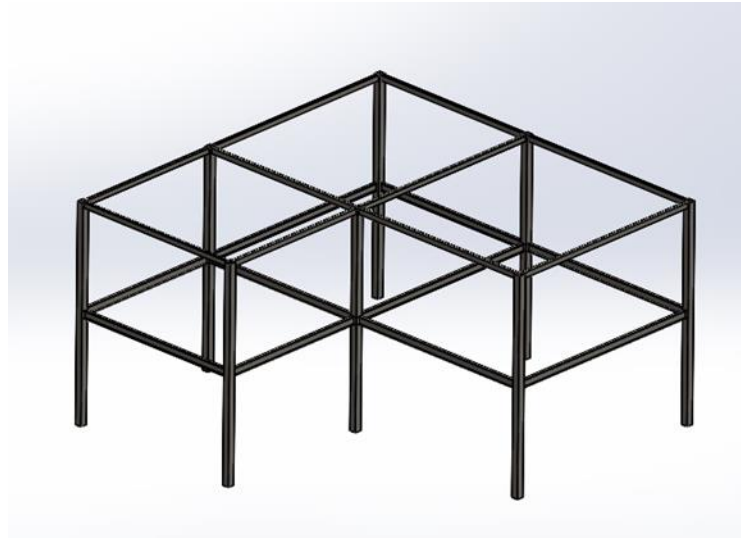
Estructura metálica diseñada en SOLIDWORKS
